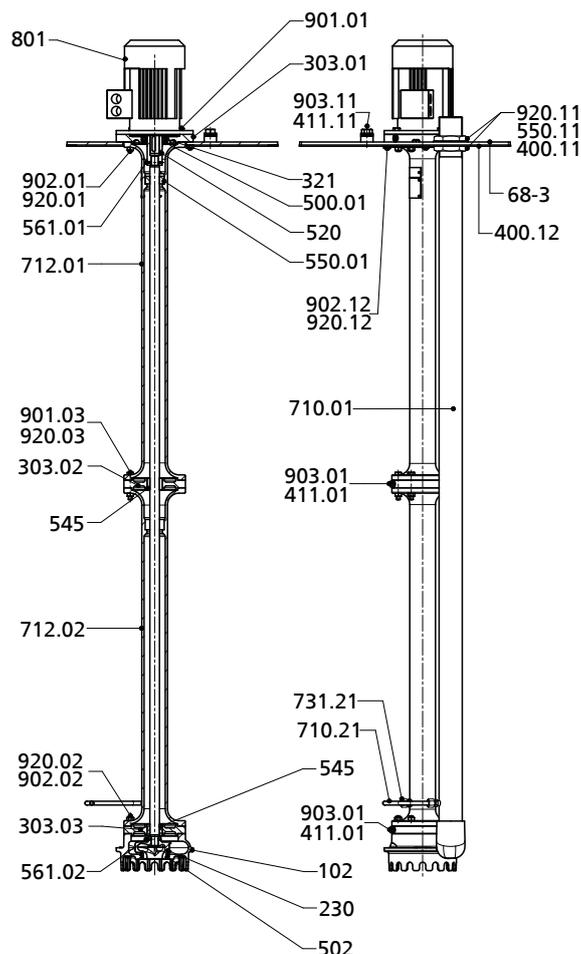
Чертеж МК, МКА - глубина установки 1900 мм - смазка собственной жидкостью
